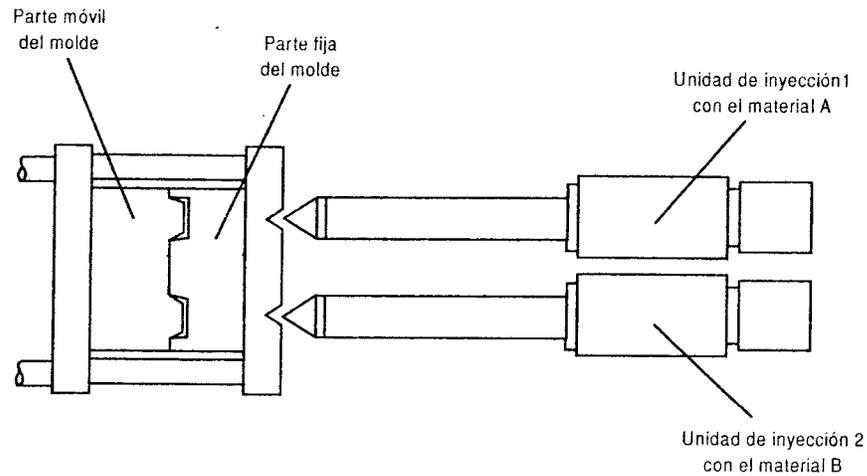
Máquina de inyección multicolor de diseño horizontal.
